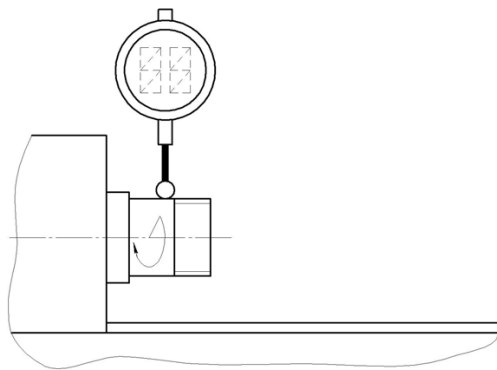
Схема установки индикатора для проверки радиального биения на центрирующей шейке шпинделя
